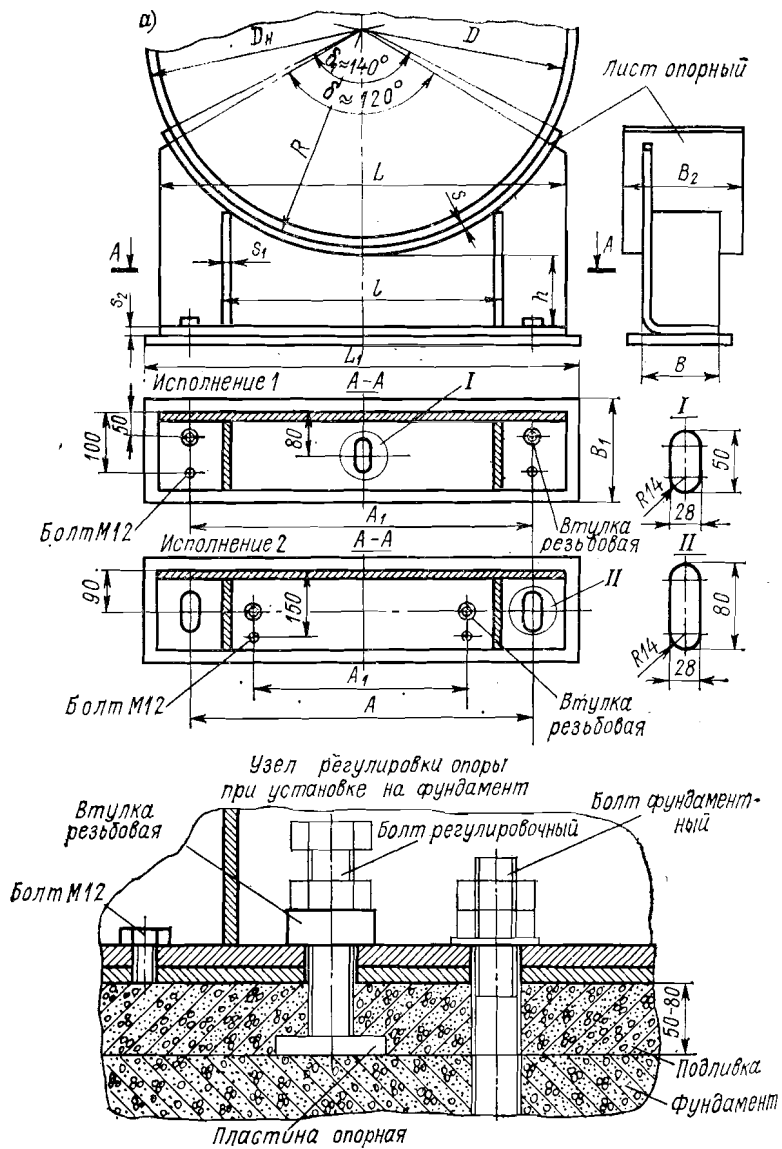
Конструкции стандартных седловых опор под стальные сварные го
